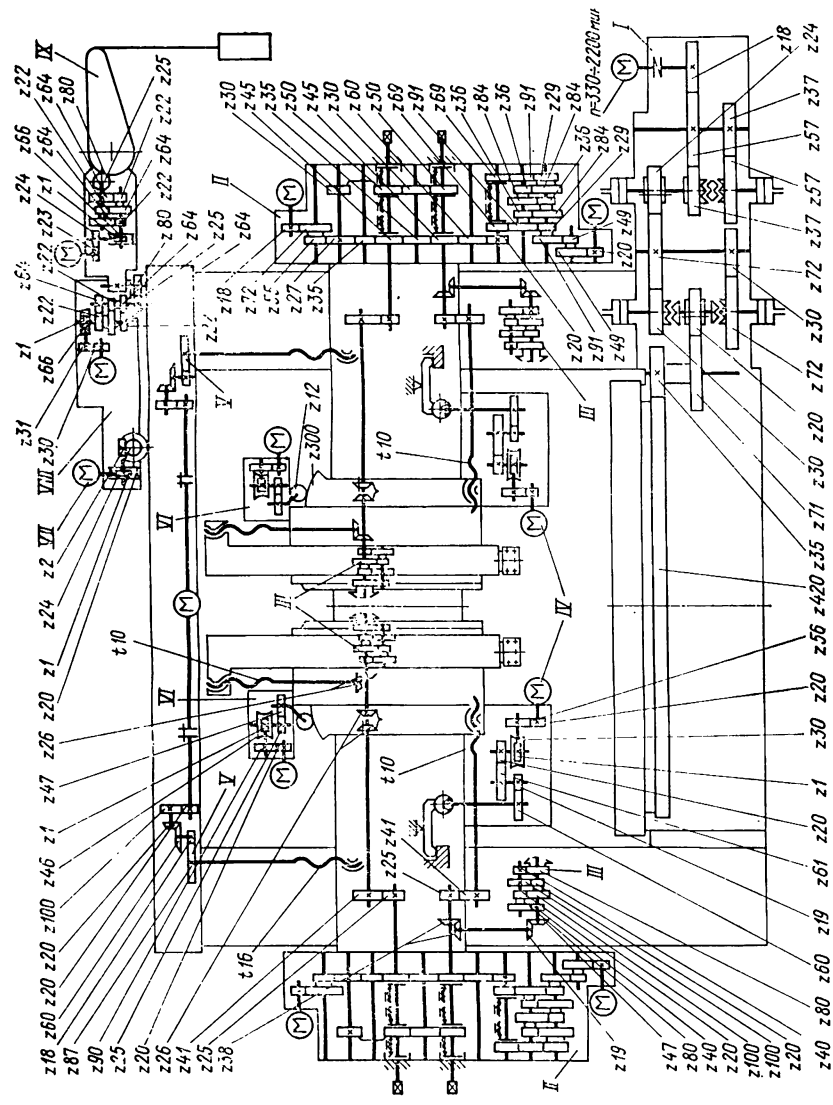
Кинематическая схема токарно-карусельного двухстоечного универсального станка мод. 1580Л.
